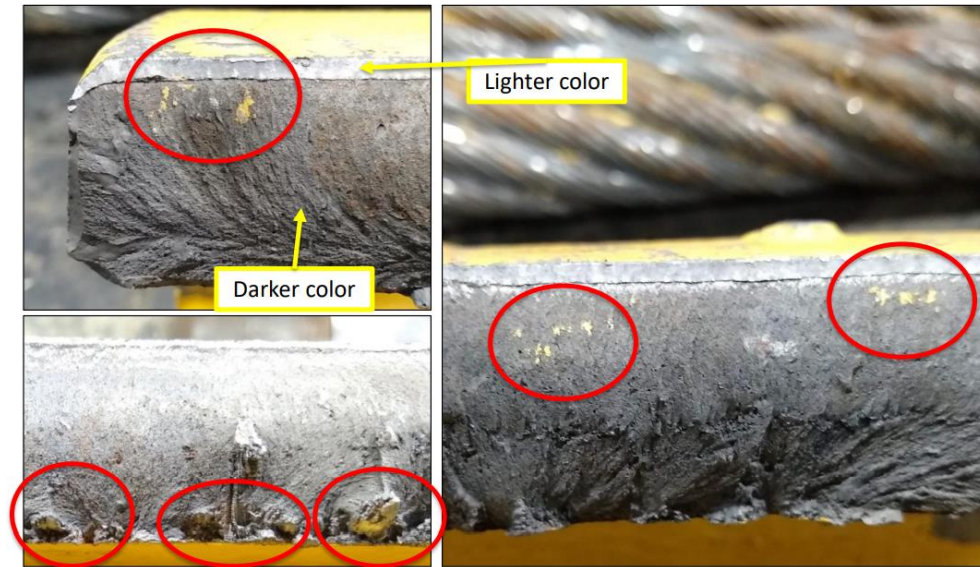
Superficie de la fractura y las zonas donde podemos ver que la pintura de la pieza entro a la grieta antes de que esta fracturara por completo.
